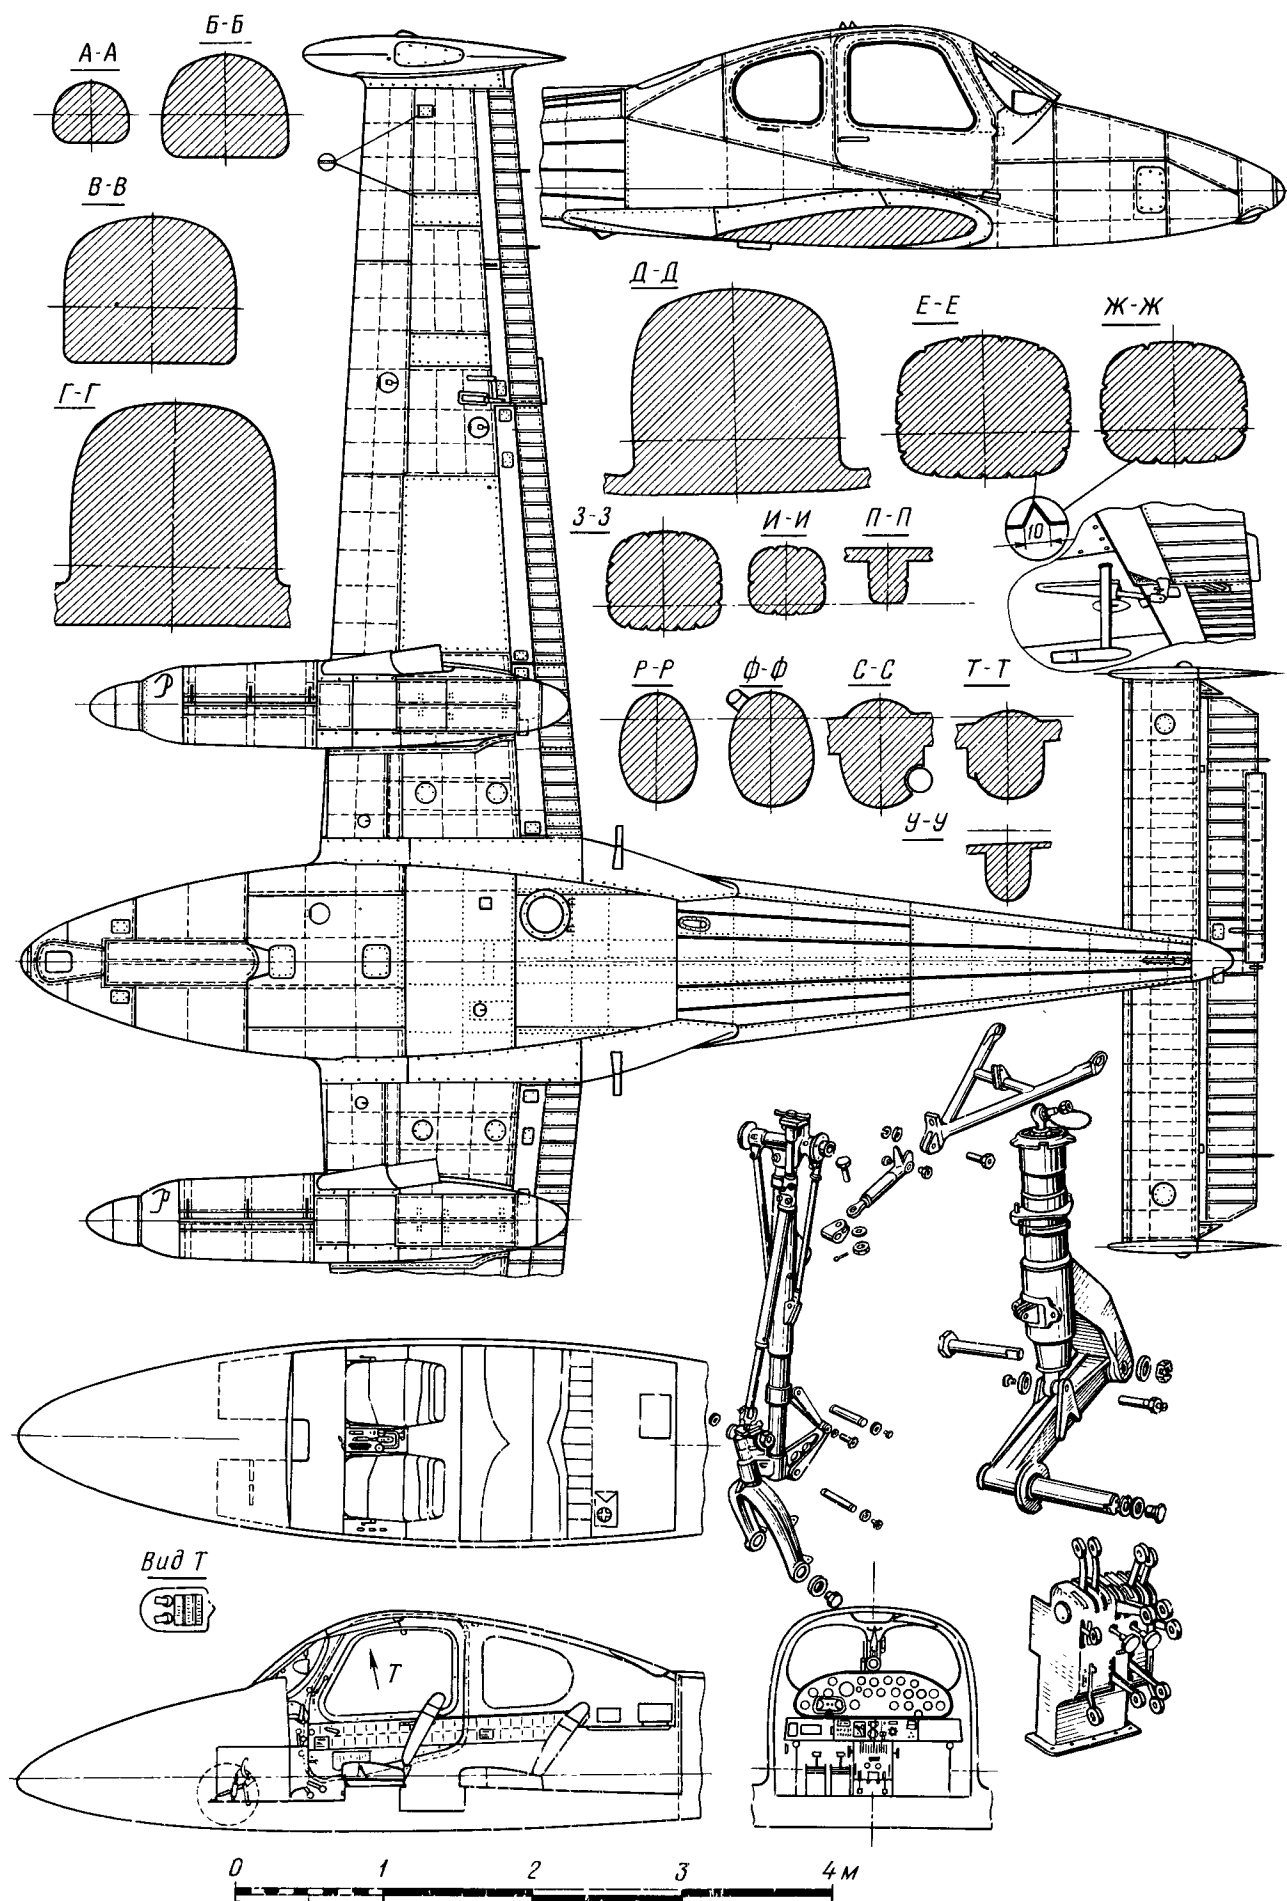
Детали конструкции и оборудования самолета ИЛ-200 Д «Мераз»
